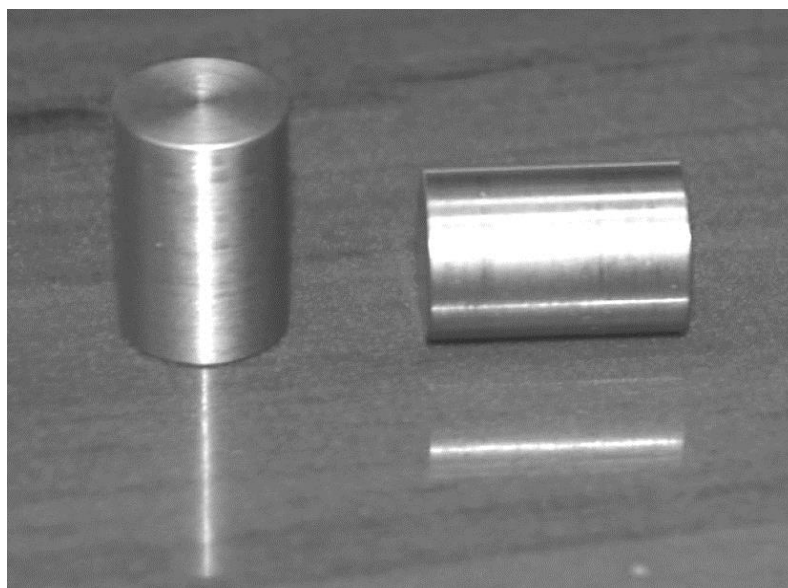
Цилиндрические образцы для испытания на сжатие
